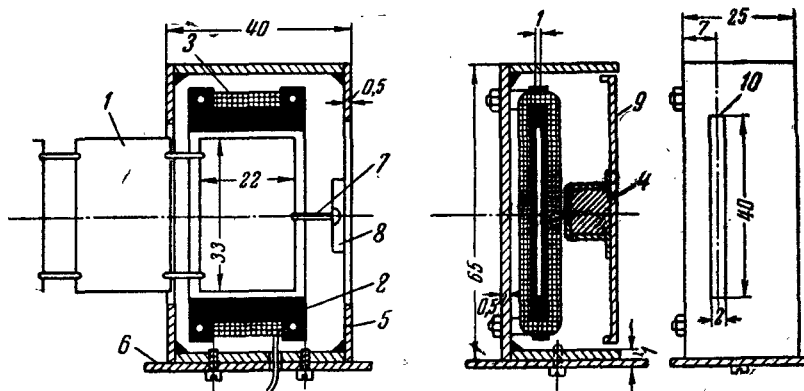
Эскиз конструкции магнитоотрицательного преобразователя. 1 — пластинка фильтра; 2 — каркас катушки; 3 — высокочастотная обмотка; 4 — магнит; 5 — экран; 6 — шасси; 7 — четвертьволновая связка; 8 — бортик; 9 — крышка; 10 — щель в экране.
